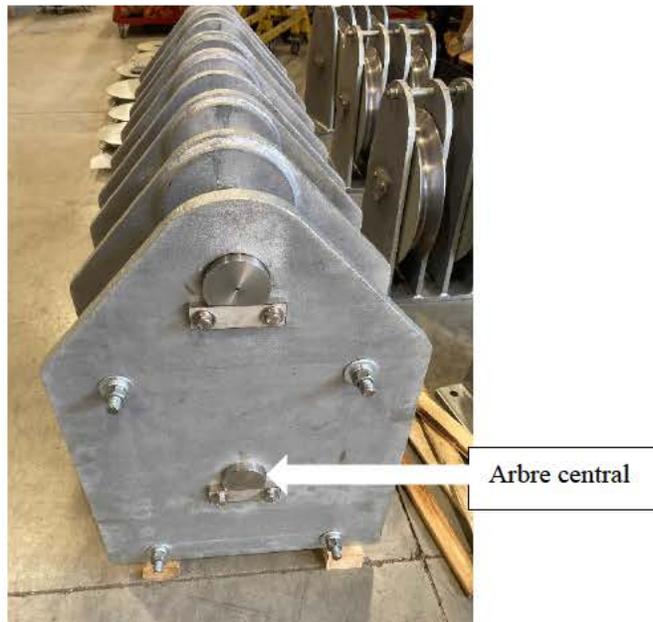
Moufle de levage inférieur assemblé (vue de côté)
